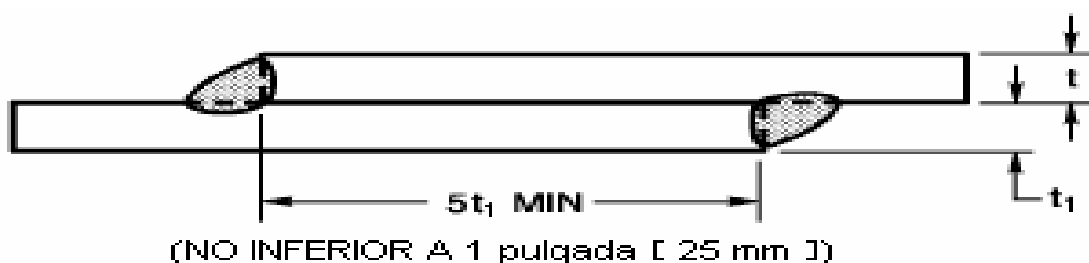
Configuración y detalles de la Unión (Uniones Soldadas en Filete)
